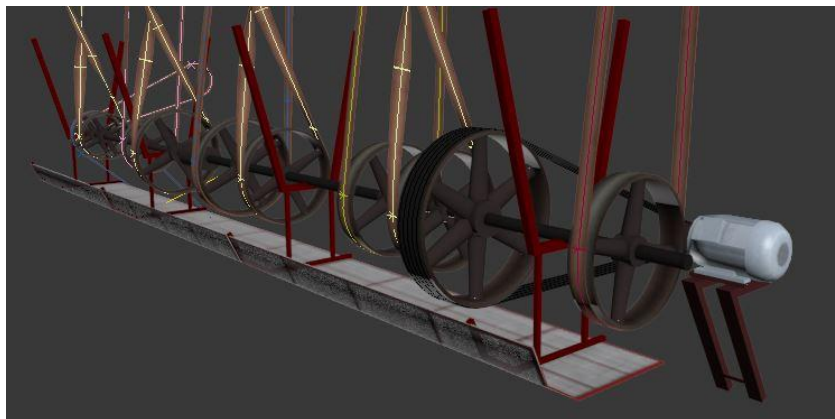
Vista del sistema de transmisión de la planta baja texturizado.
